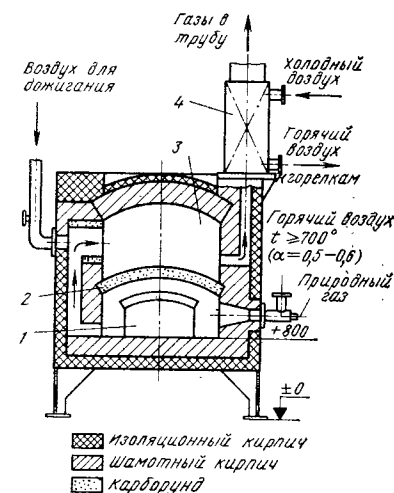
Малая рекуперативная печь для безокислительного нагрева заготовок открытым пламенем:
